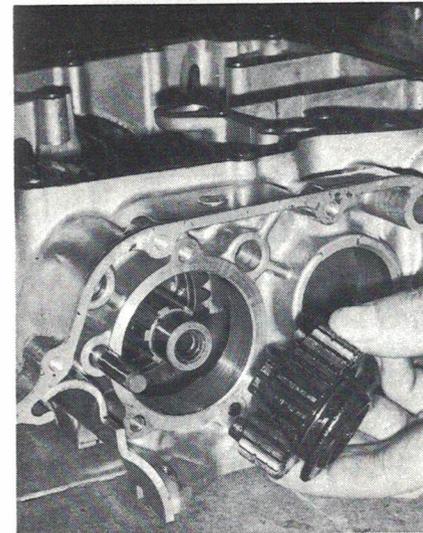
Retrait du pignon secondaire de 5e (Photo RMT)
